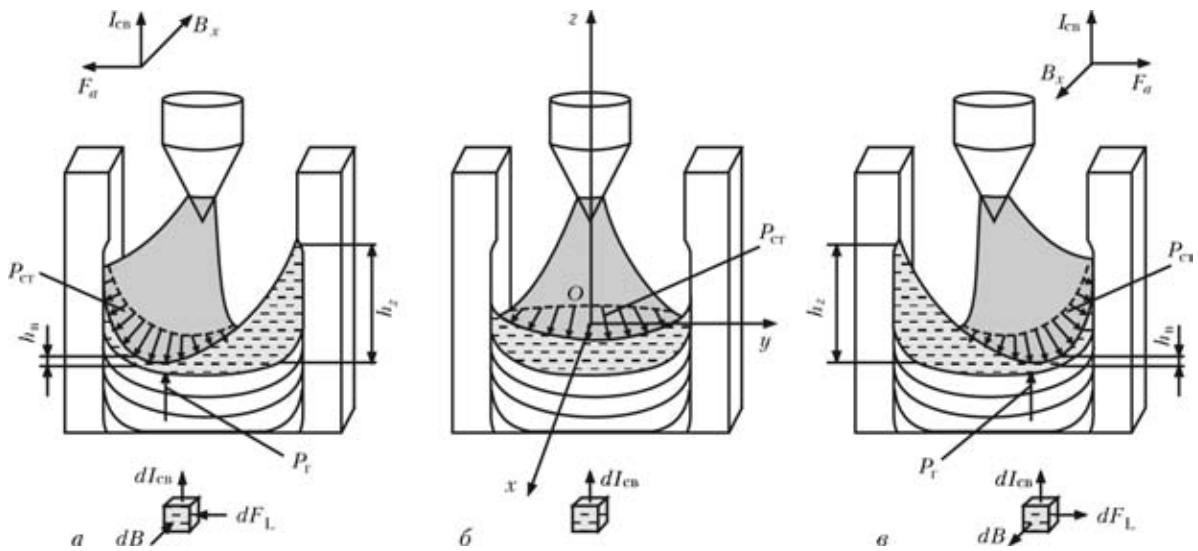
Схема оплавления боковых стенок разделки и расположение сварочной дуги в крайних (а, в) и промежуточном (б) положениях
